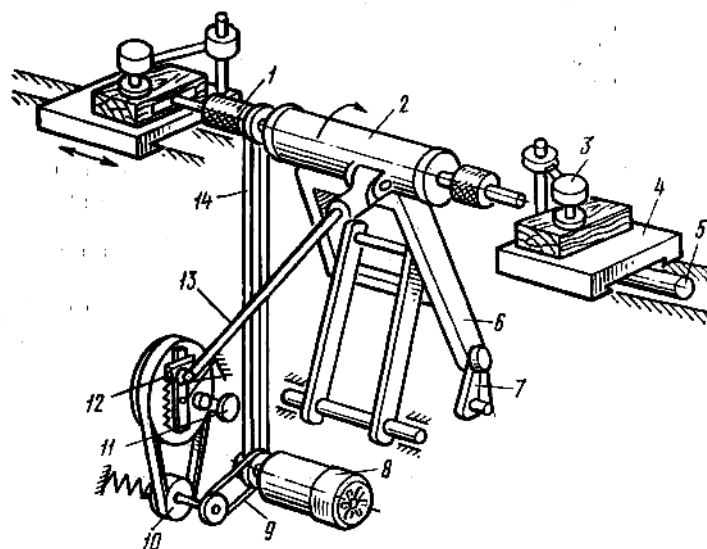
Кинематическая схема сверлильно-пазовального станка:
